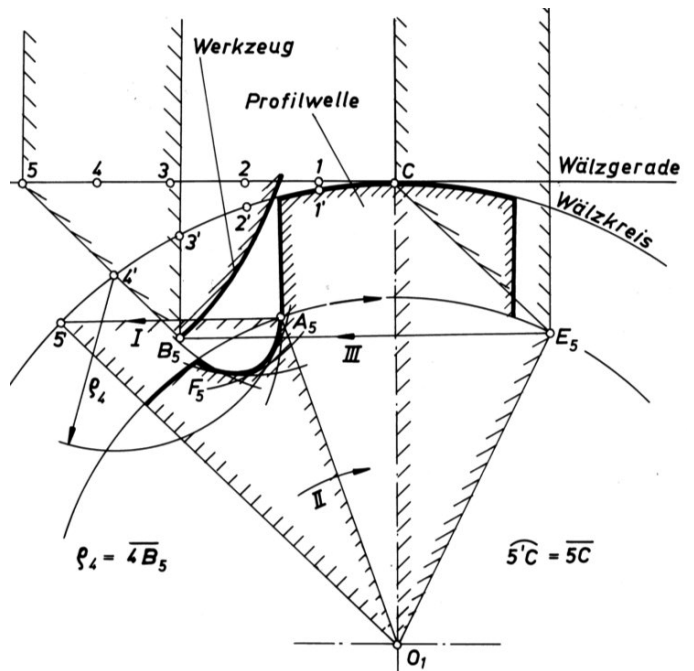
/26 Konstruktion des Abwälzwerkzeugs für ein gegebenes geradflankiges (Keil-)Wellenprofil
